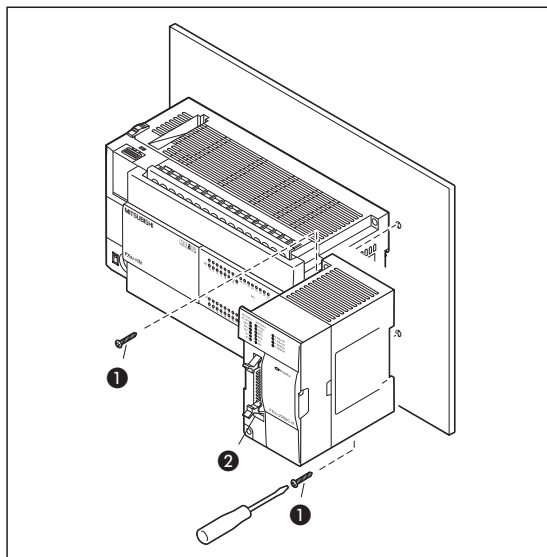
Nachdem Sie alle Befestigungslöcher gebohrt haben, befestigen Sie das Modul mit M4-Gewindeschrauben oder 4 mm Blechschrauben (① in der Abbildung links).
